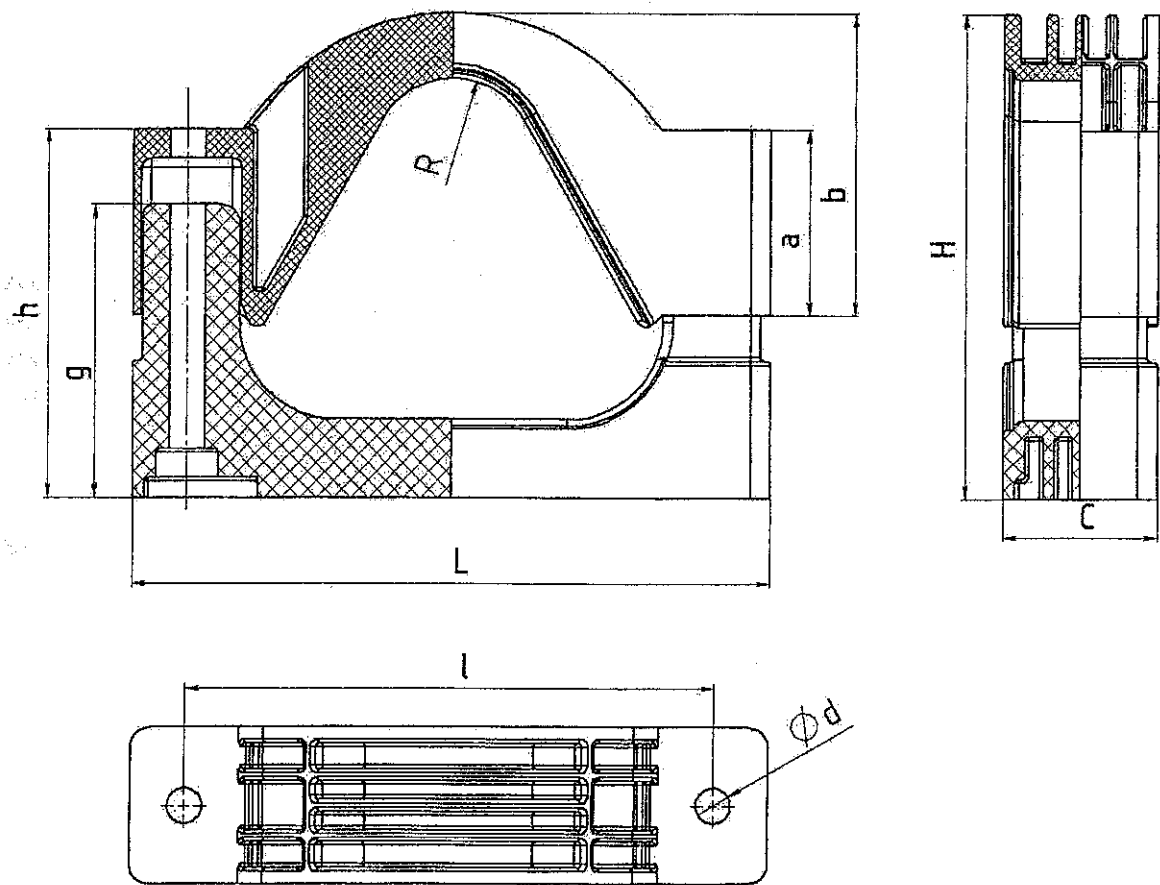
Габаритные размеры и внешний вид высоковольтного кабельного крепления марки ВККЗ
